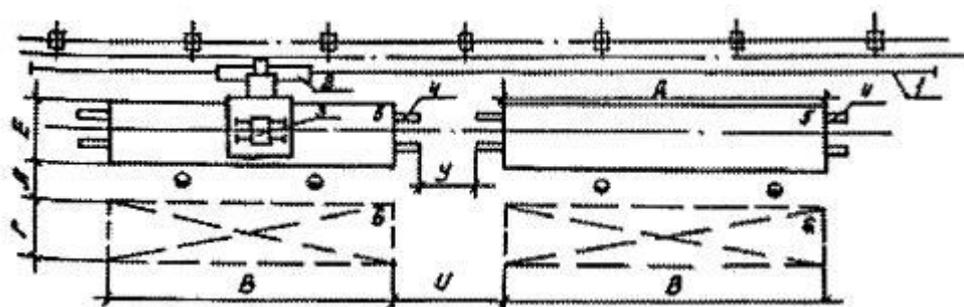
Размещение установки велосипедной тележки для автоматической сварки продольных и кольцевых швов цилиндрических изделий:
